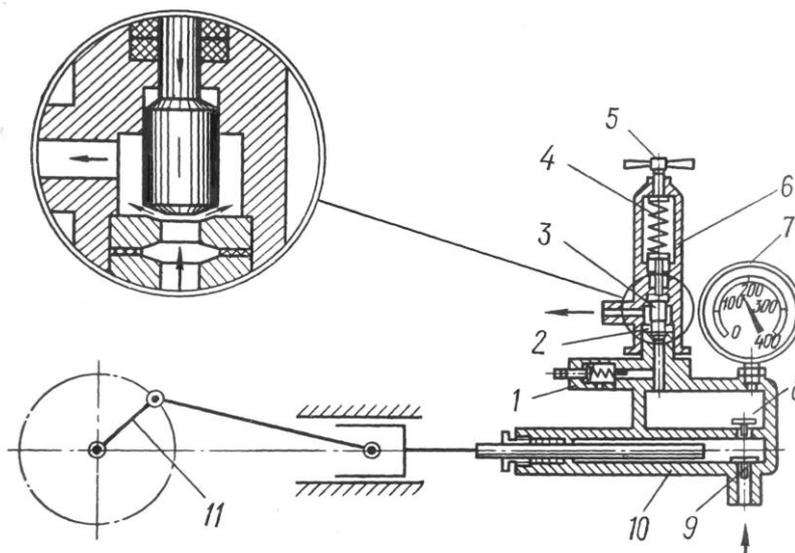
Гомогенизатор клапанного типа: 1 – предохранительный клапан; 2 – седло клапана; 3 – клапан; 4 – пружина; 5 – регулировочный винт; 6 – гомогенизирующий клапан; 7 – манометр; 8 – нагнетательный клапан; 9 – всасывающий клапан; 10 – насос; 11 – кривошипно-шатунный механизм
